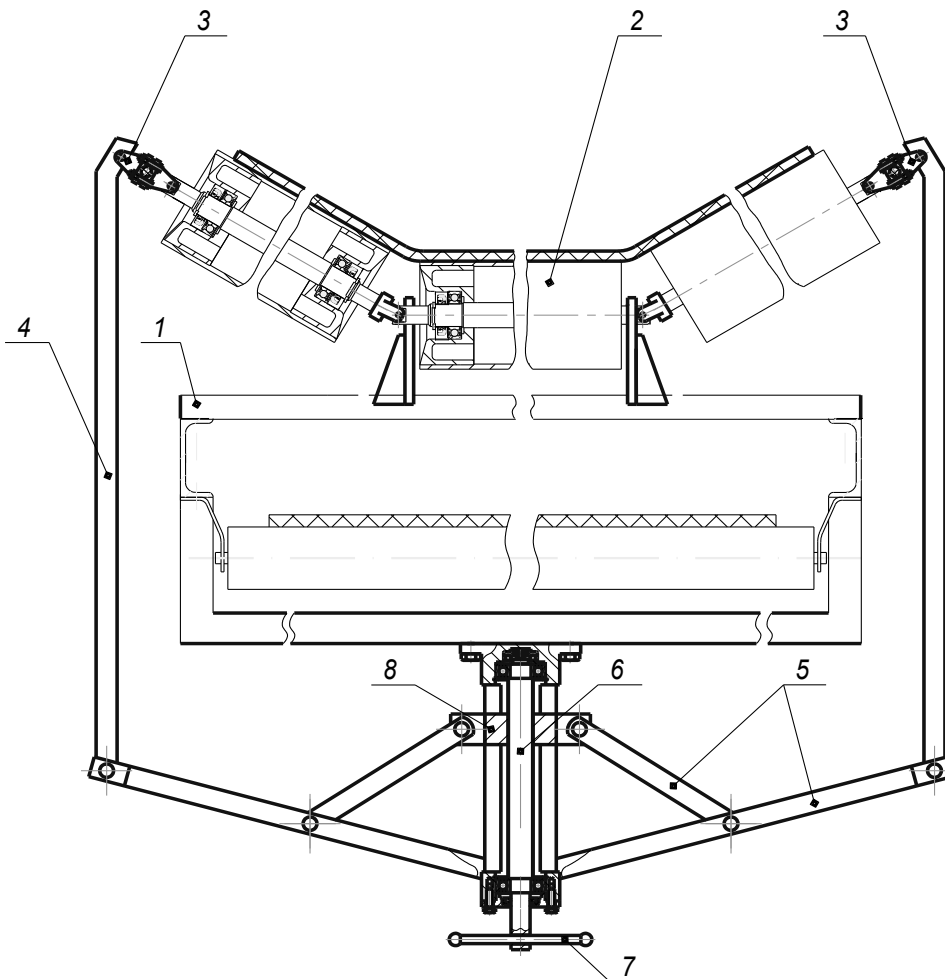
Поперечний переріз стрічкового конвеєра: 1 – остов; 2 – трироликів опора; 3 – канат; 4 – важелі; 5 – тяга; 6 – передача гвинт-гайка; 7 – маховик; 8 – гайка; 9 – стрічка.
